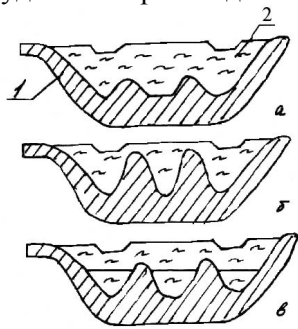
Конструкции изложниц для машинной разливки ферросиликомарганца: а - стандартная; б - стержневая; в - ячеистая; 1 - изложница в разрезе; 2 - сплав
